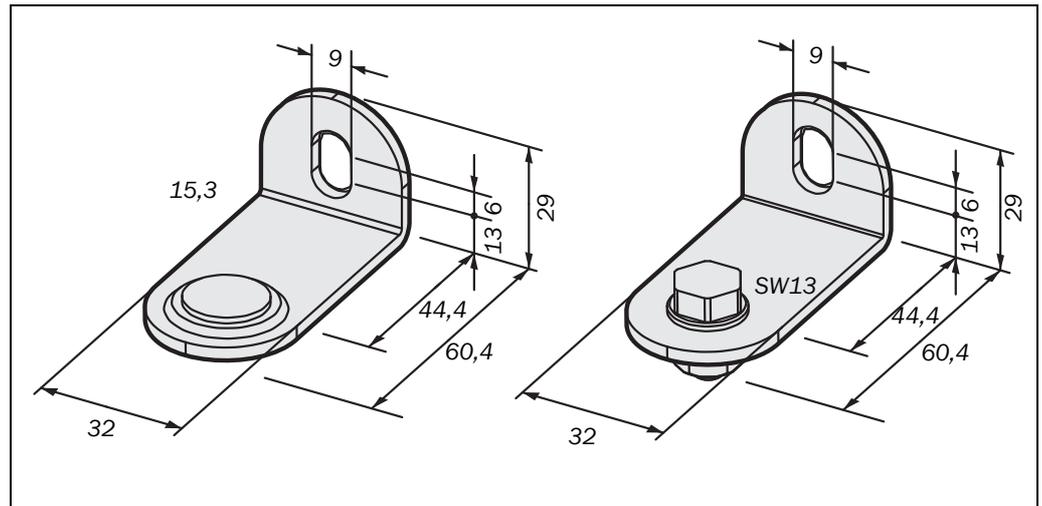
disegno quotato del supporto su guida laterale (mm)
